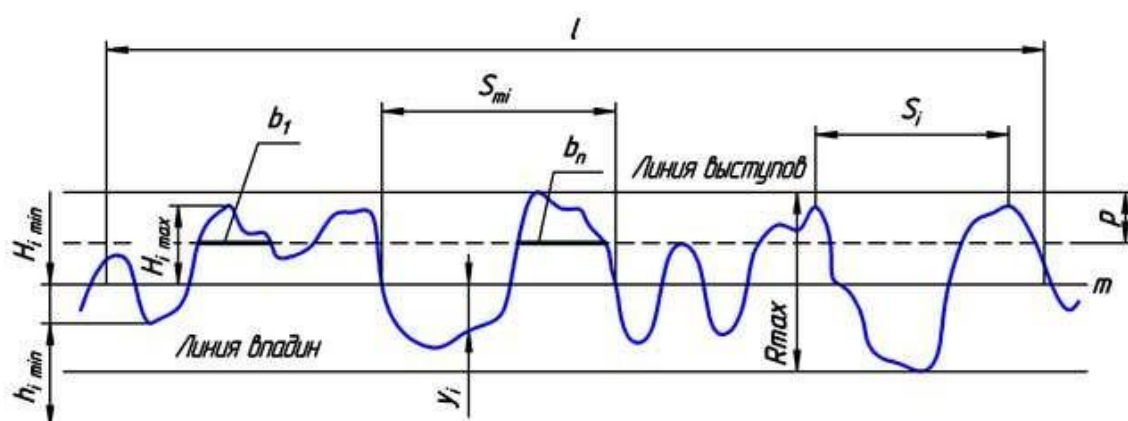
Нормальный профиль и параметры шероховатости поверхности
